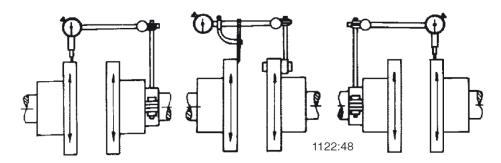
Проверка центровки муфты с проставкой с помощью индикатора
